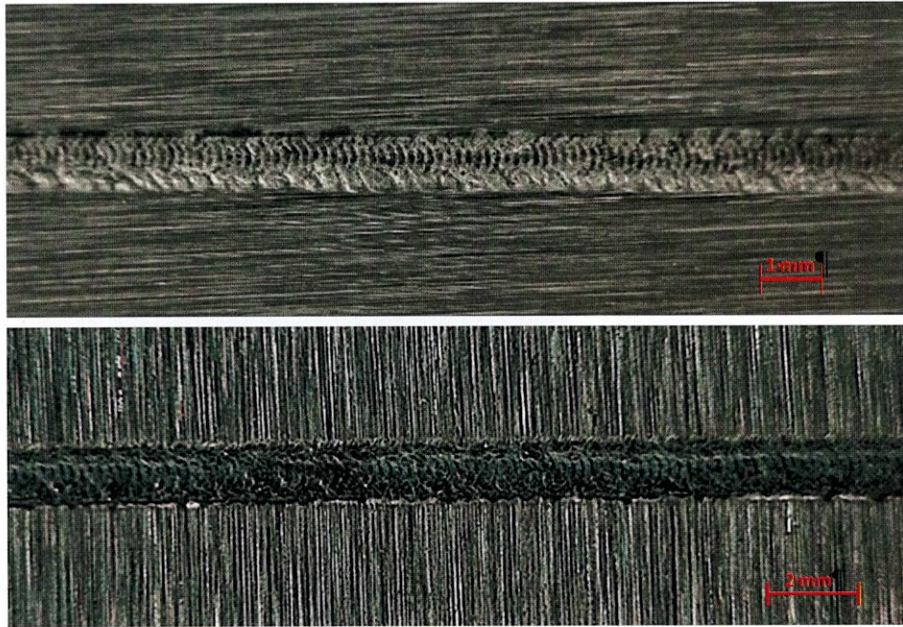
• Oberseite (oben) und Wurzelseite (unten) einer laserstrahlgeschweißten I-Naht am Mg/Mg-Stumpfstoß.
